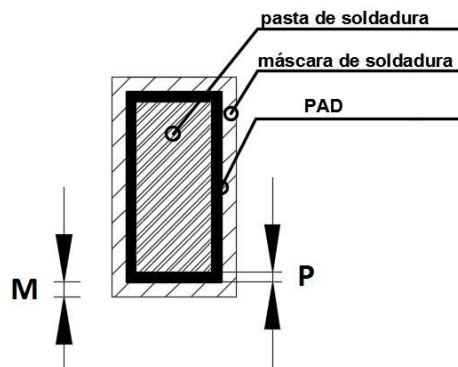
Márgenes de pasta de soldadura (P) y máscara de soldadura (M) en un pad
